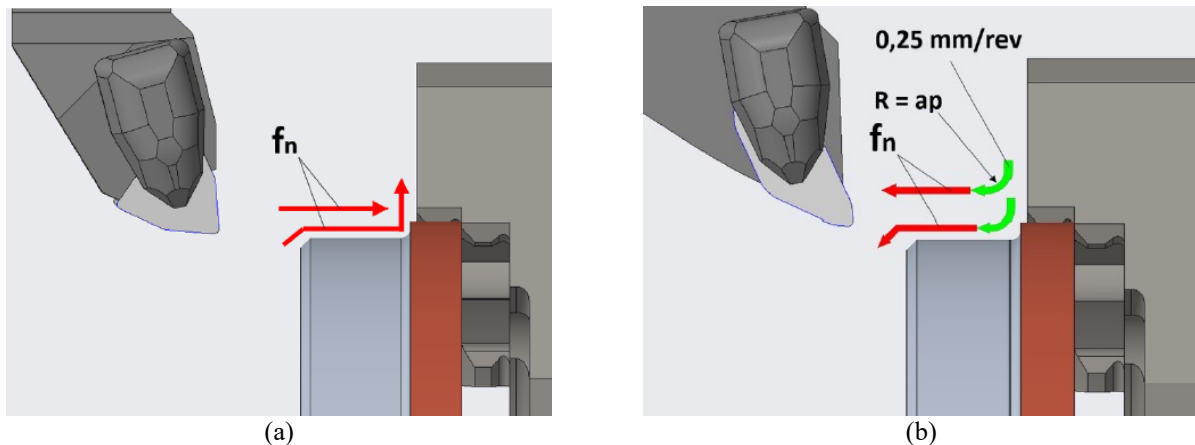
Trajetória da ferramenta na usinagem em torneamento convencional (a) e em alto avanço (b).
